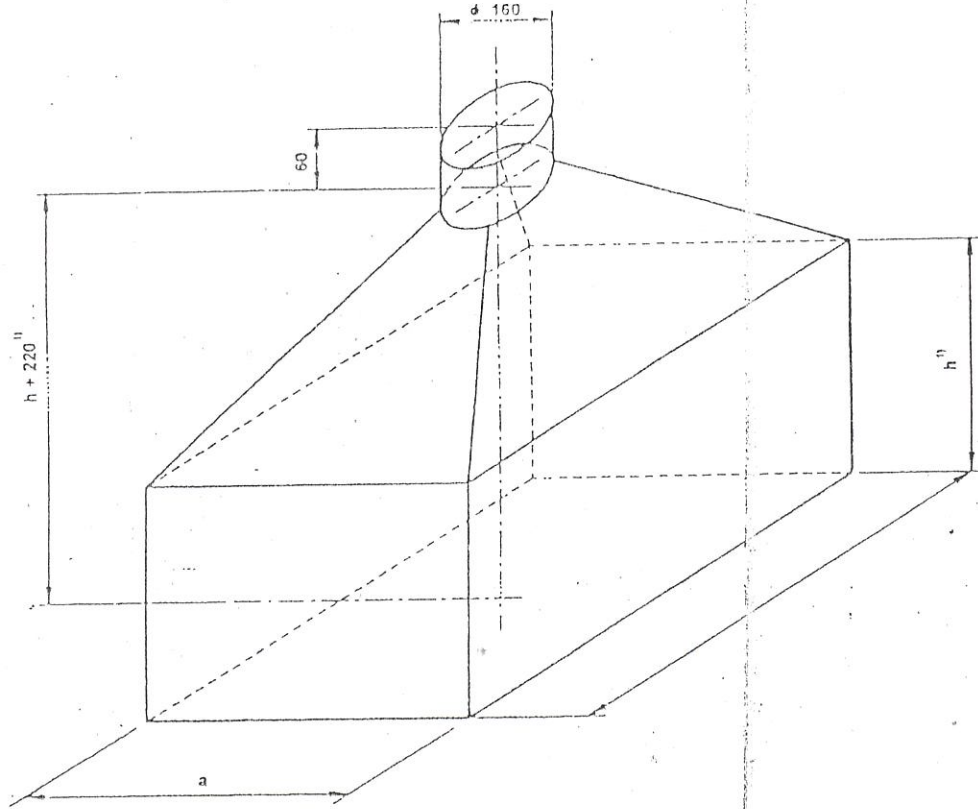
Dispositivo de ensayo de la combustión de cada quemador individual
